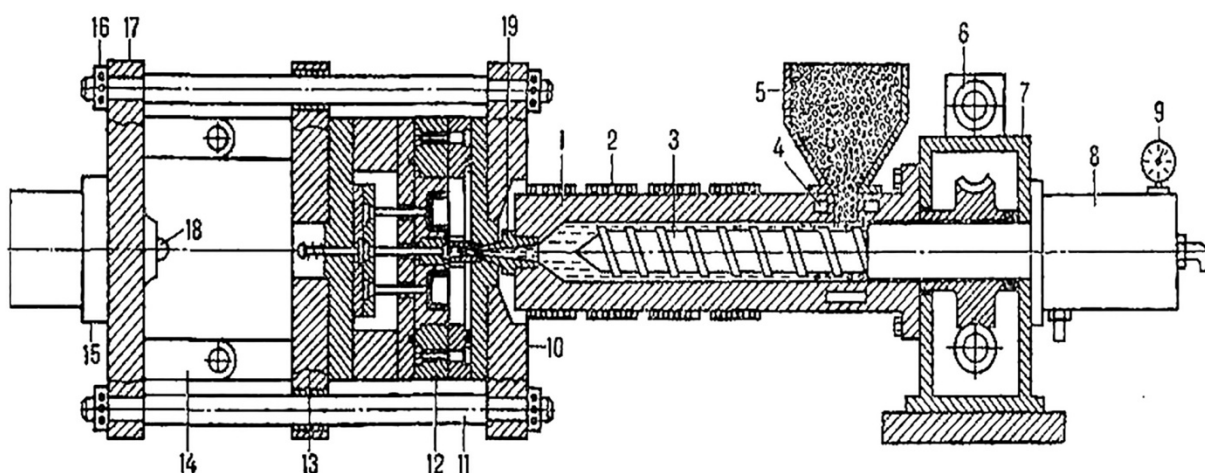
Литьевая машина: 1 -материальный цилиндр; 2 -нагревательные элементы; 3-винт (шнек); 4-каналы охлаждения; 5-бункер для материала; 6-гидродвигатель; 7-редуктор; 8-гидроцилиндр узла впрыска; 9-манометр; 10, 17-неподвижные плиты; 11 - направляющие колонки; 12-литьевая форма; 13-подвижная плита; 14-колесно-рычажный механизм; 15-гидро-цилиндр узла смыкания; 16-гайки; 18-упор; 19-сопло.
